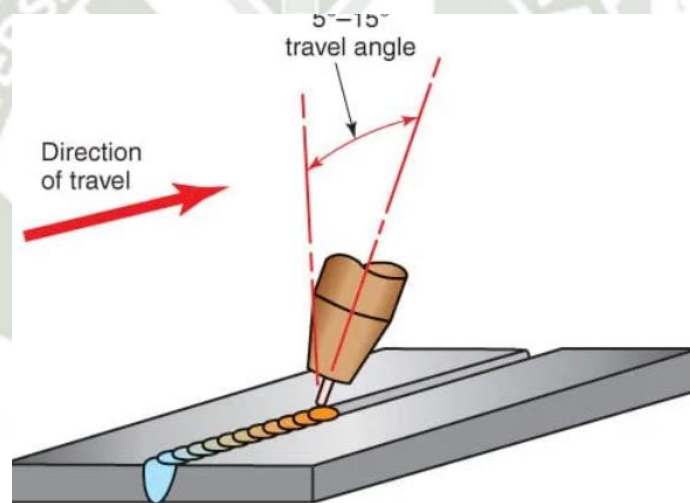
Representación de la soldadura tipo filete por posición plana
